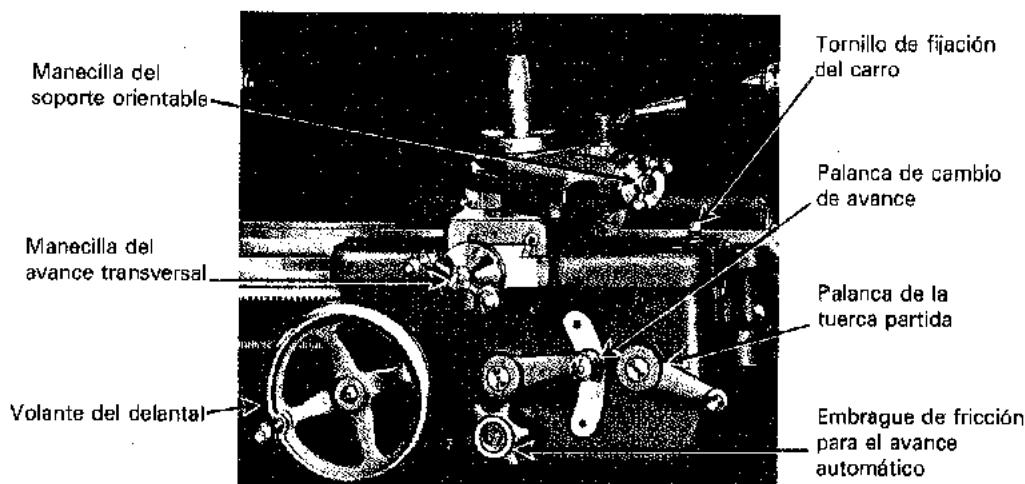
Elementos más importantes del carro del torno (South Bend Lathe Works).
